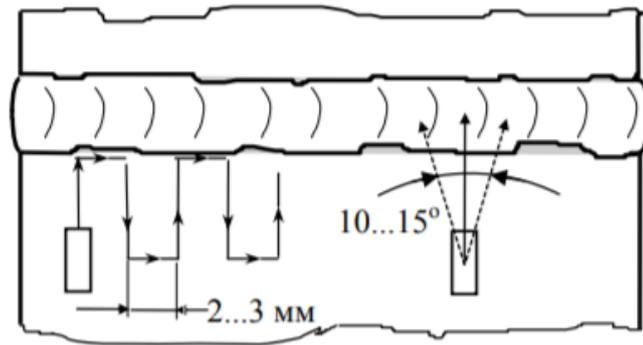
ультразвуковой контроль стыкового сварного соединения [14]
